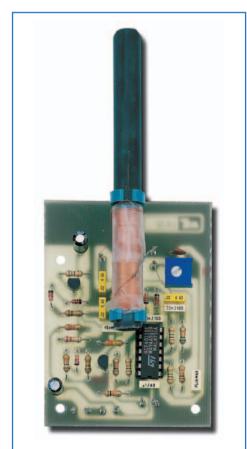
Photo du prototype de la platine du testeur de bobinage.
